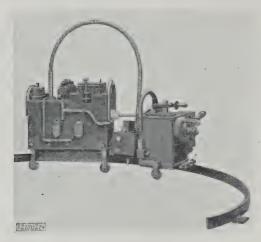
Schweißwagen mit Schienenführung in beliebiger Krümmung der Firma Elin, Weiz.
